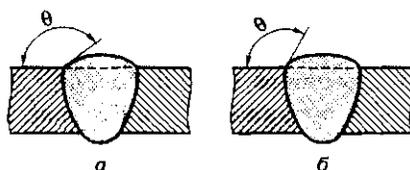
Правильный (а) и неправильный (б) профили сварного шва:
